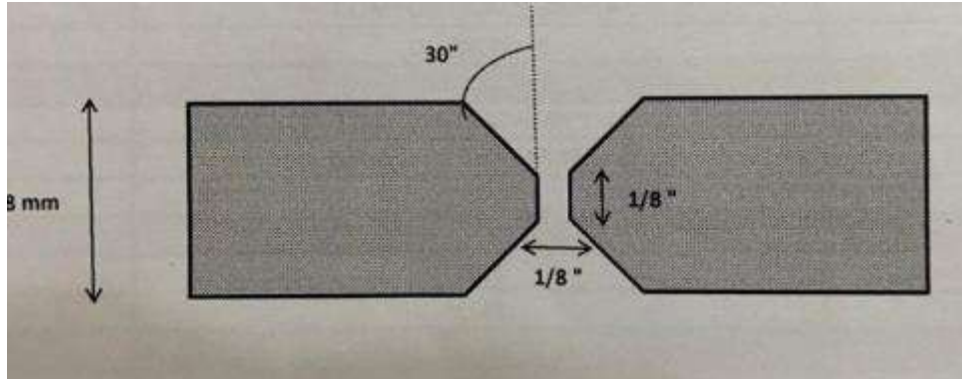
Dimensiones de soldadura de doble bisel.
